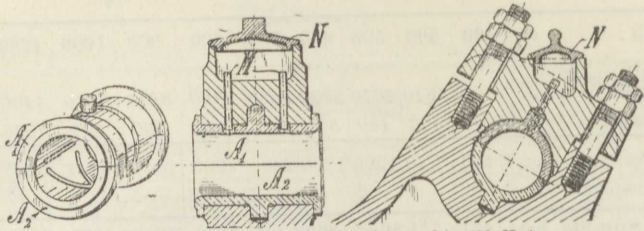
Hauptlager für Maschinen bis 400 Hub.
